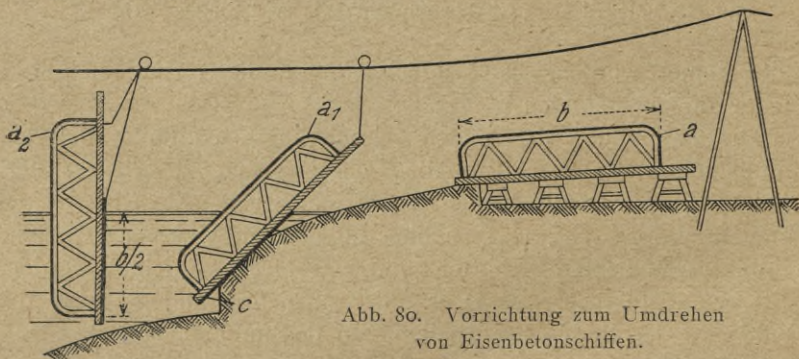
Vorrichtung zum Umdrehen von Eisenbetonschiffen.
